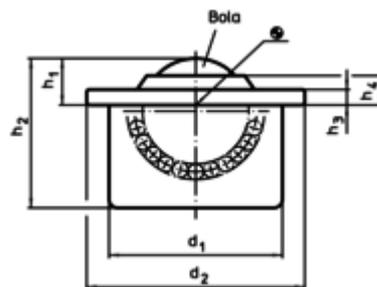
Esquema de las partes del rodamiento.
